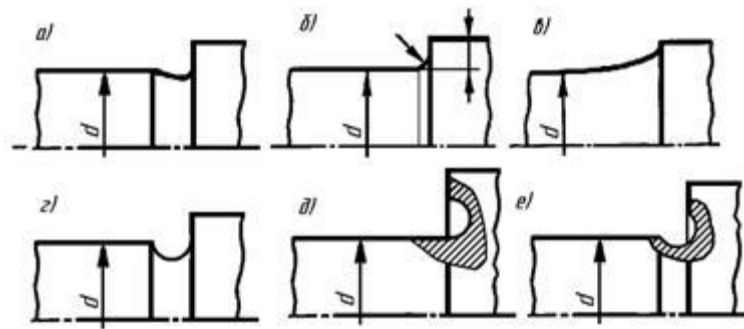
Форми перехідних ділянок між циліндричною поверхнею та заплечиком
